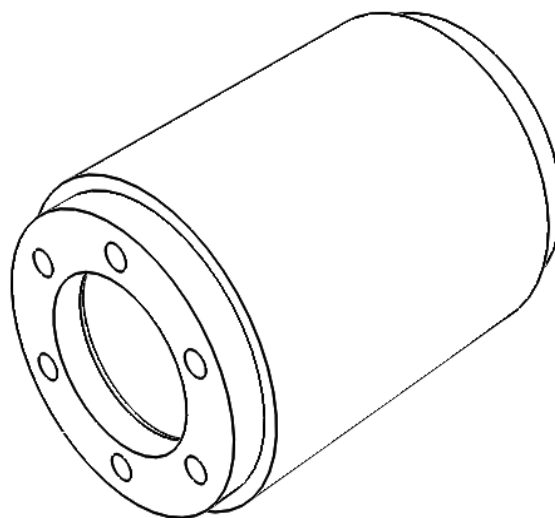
Vista em perspectiva isométrica do suporte das flanges
